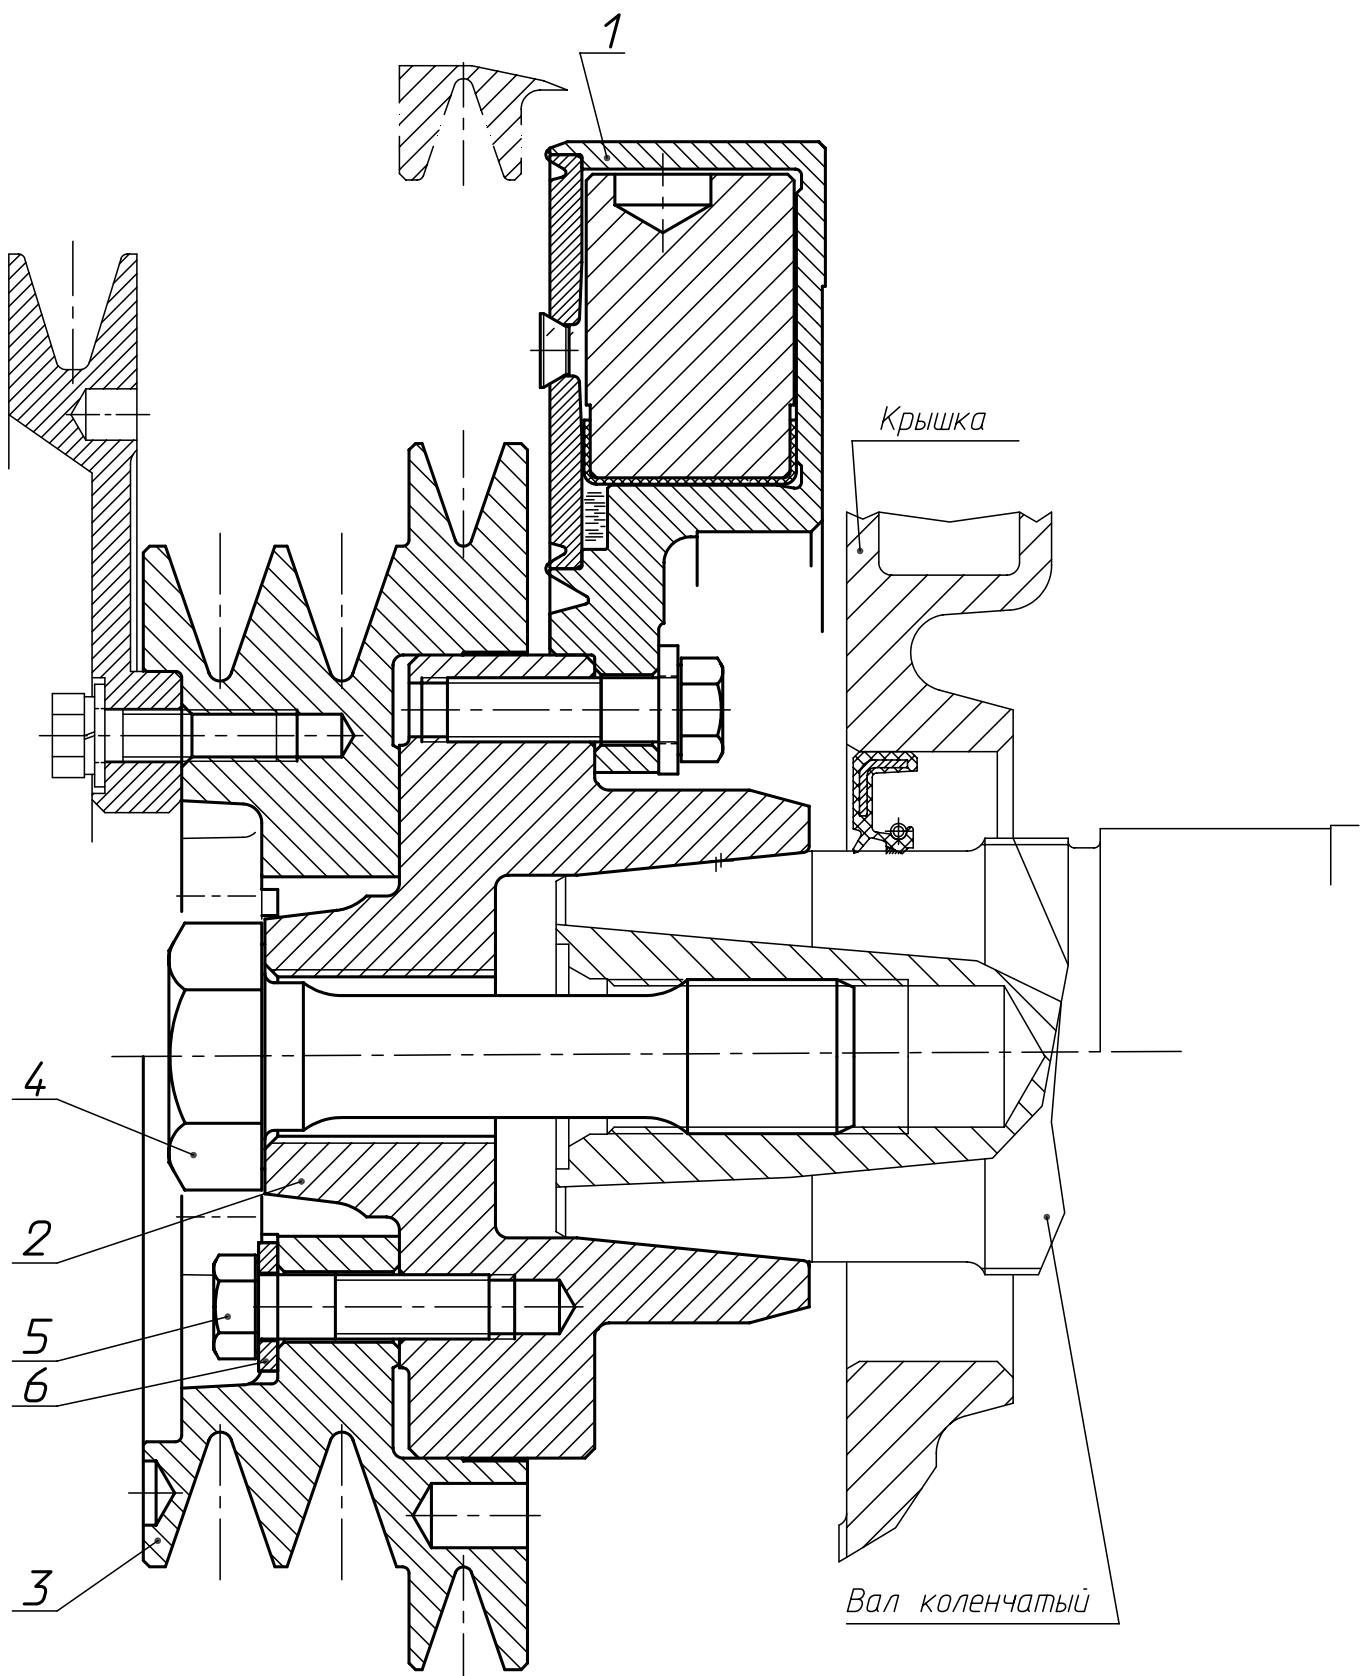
Установка гасителя и шкива на коленчатый вал двигателя типа ЯМЗ-7511
